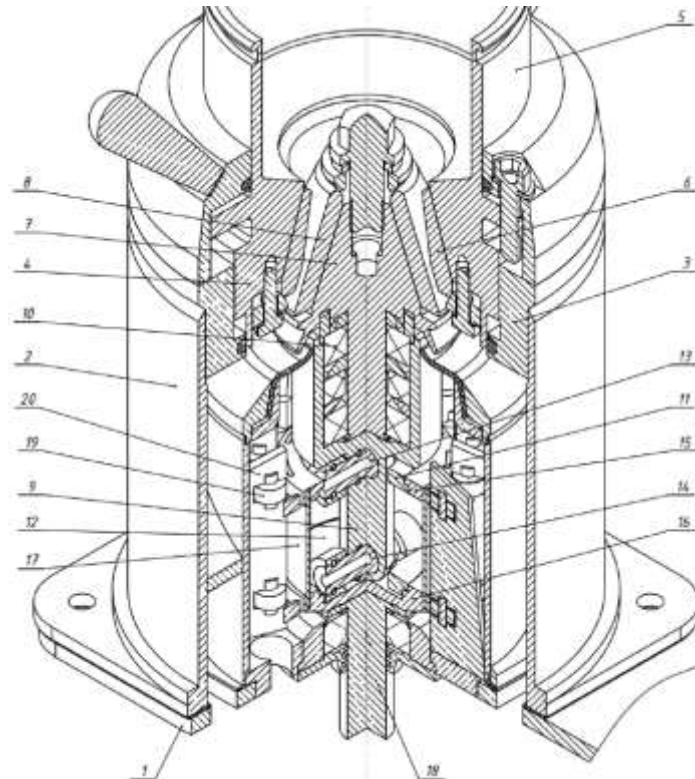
Сборочный чертеж дробилки с регулируемым эксцентриковым узлом
